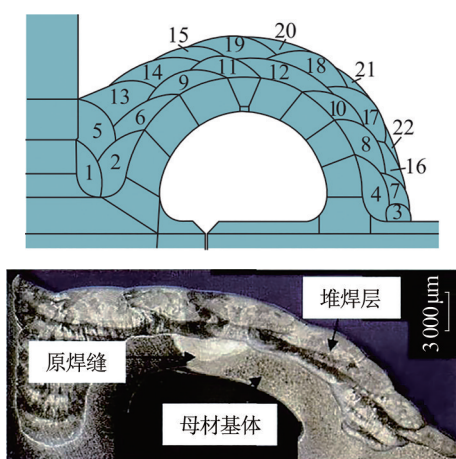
秦山核电站CRDM下部 Ω 焊缝堆焊结构和焊缝形貌^[12]
